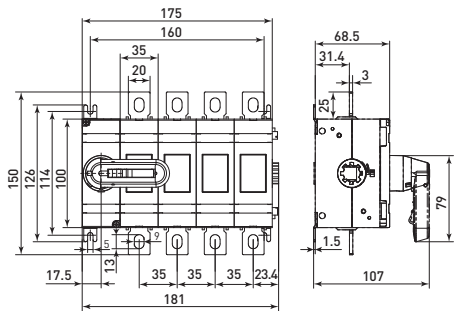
Габаритные и установочные размеры рубильников 160-250А 4Р
